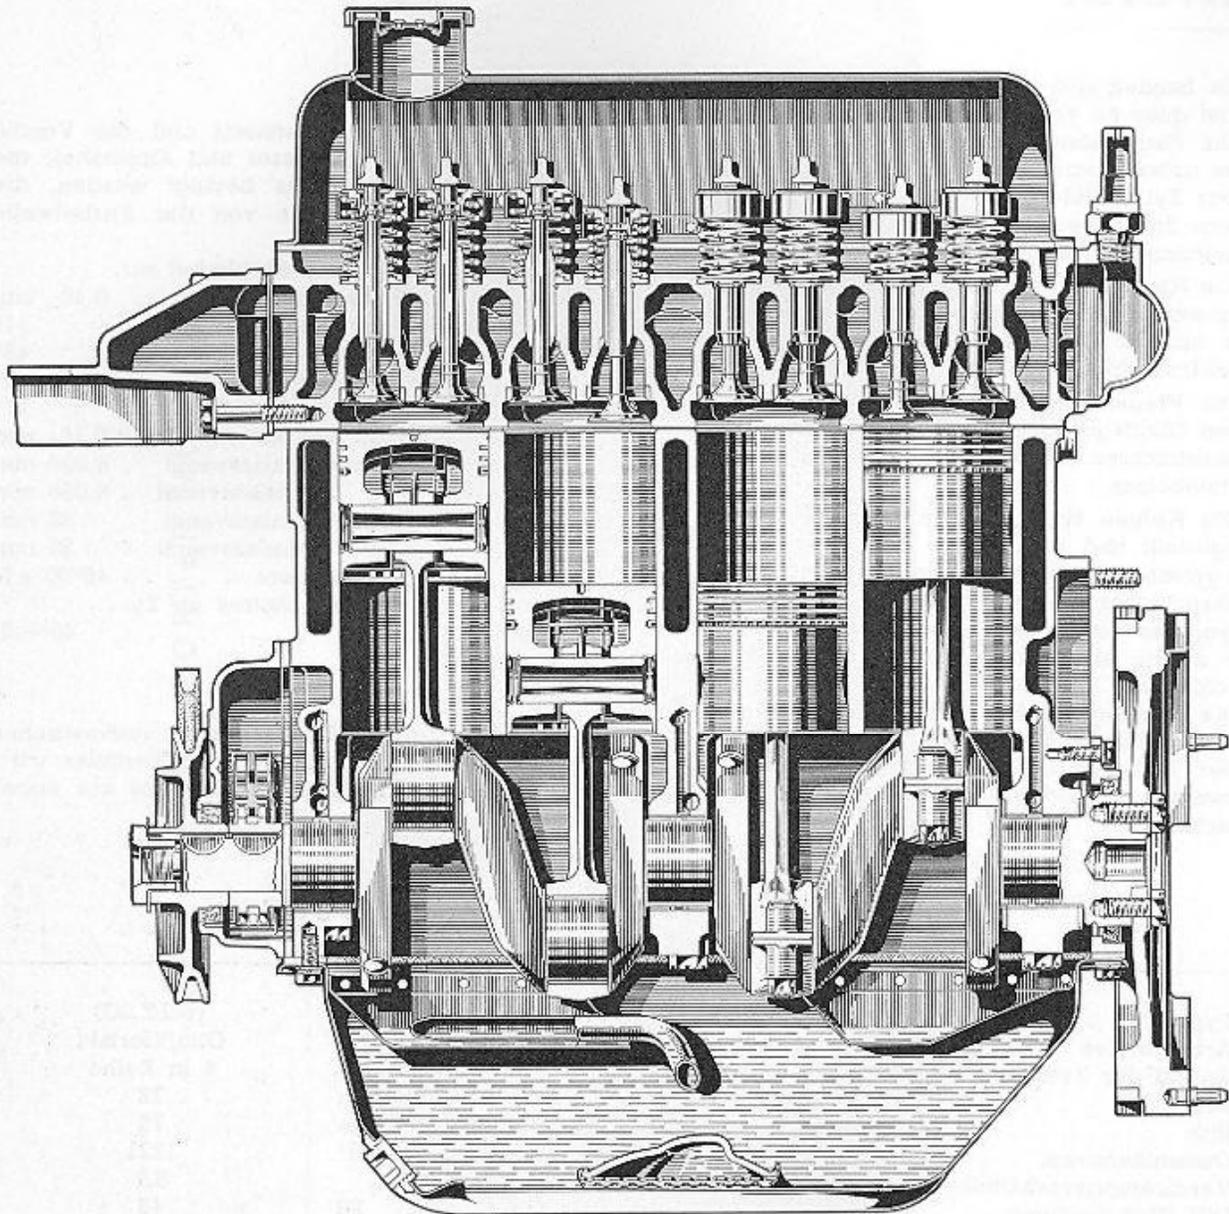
Längsschnitt durch die Zylinder des Motors Type 103LZ.000.
